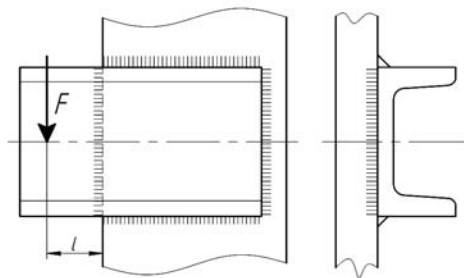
Сварное соединение швеллера к стальной плите
